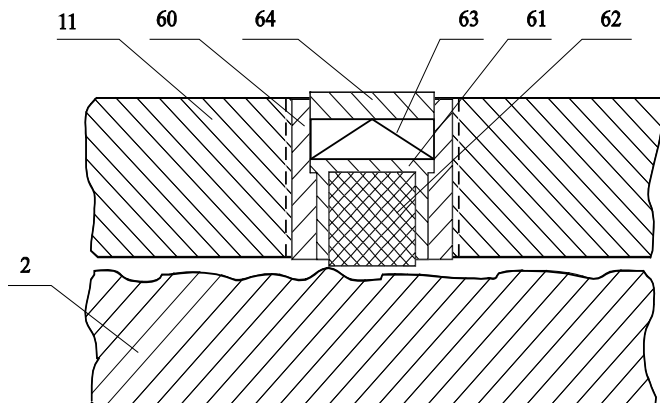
Пристрій для вирівнювання поверхонь рухомих елементів суперпрецизійної лінійної напрямної
